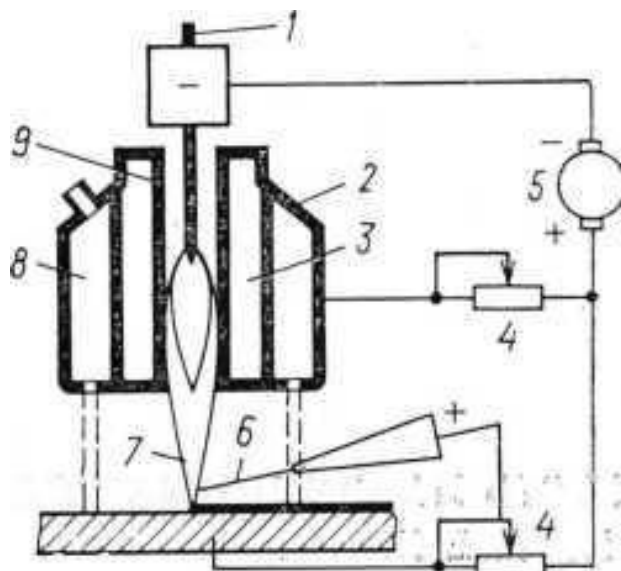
Схема плазменной наплавки с присадочной проволокой:
